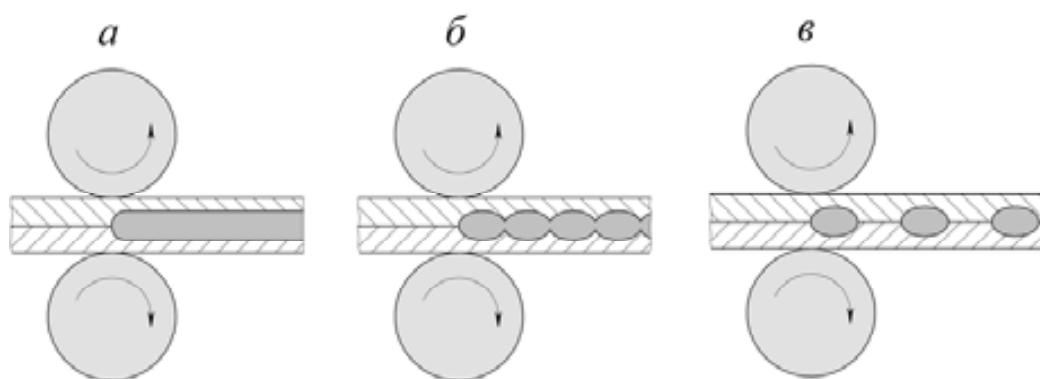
Способы шовной сварки: *а* – непрерывная; *б* – прерывистая; *в* – шаговая
